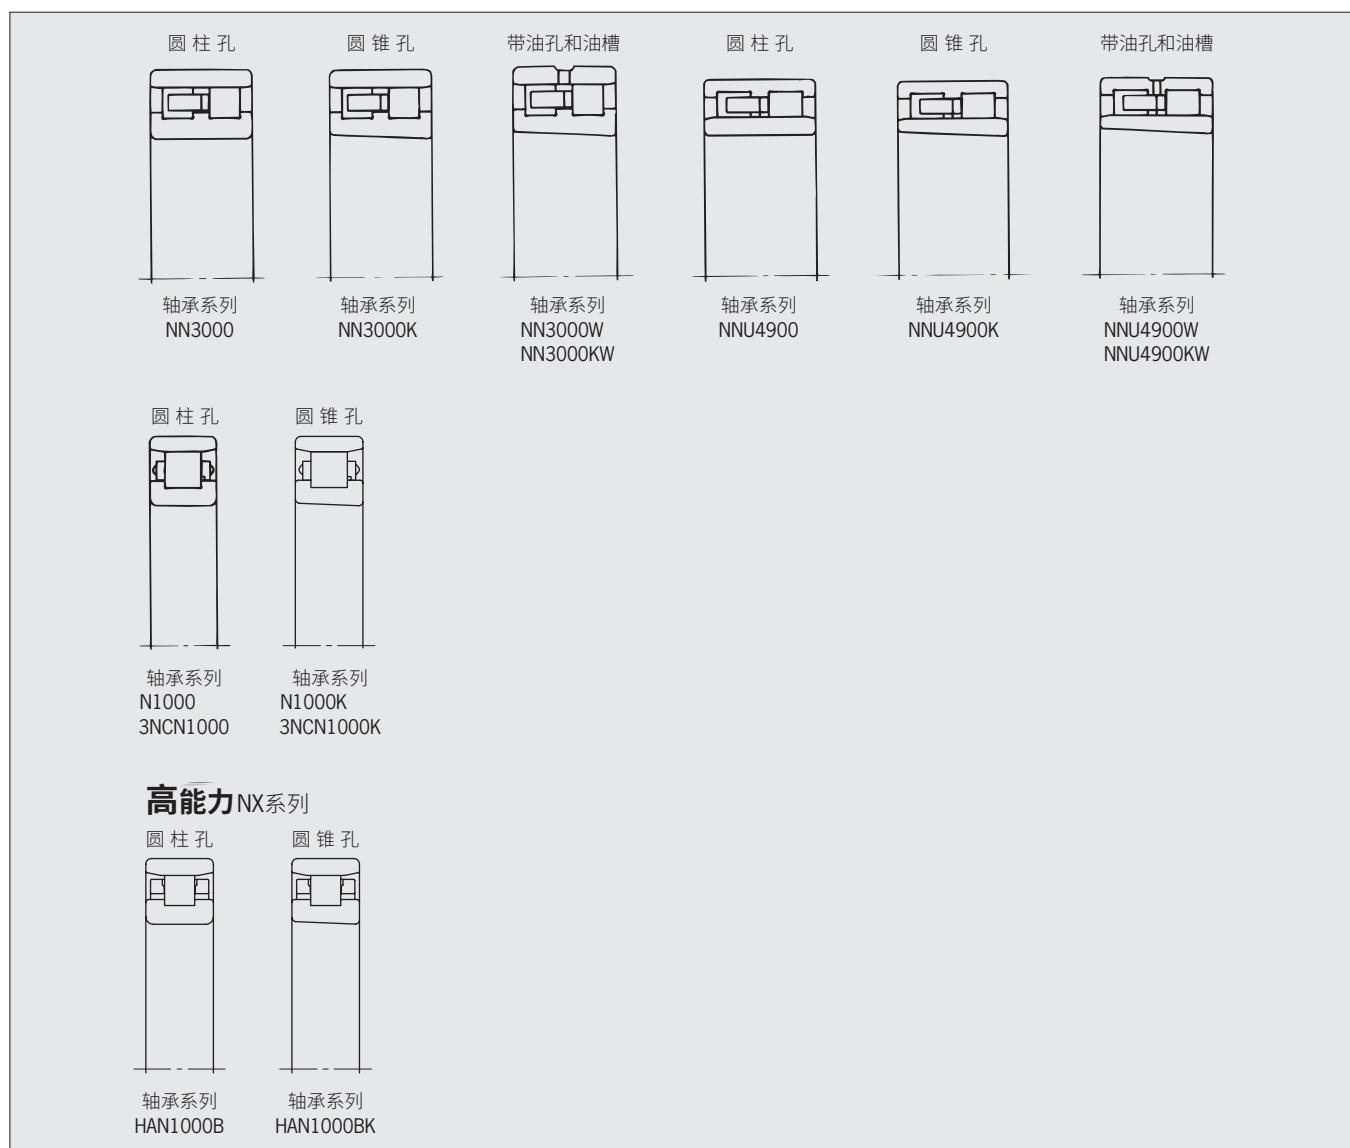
机床主轴用圆柱滚子轴承的形式和系列
